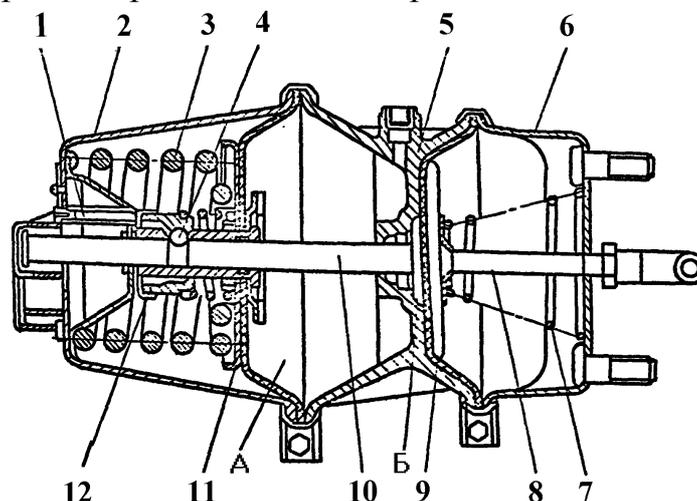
Тормозная камера с пружинным энергоаккумулятором: 1 – направляющая; 2 – цилиндр энергоаккумулятора; 3 – силовая пружина; 4 – шарик; 5 – фланец; 6 – корпус тормозной камеры; 7 – возвратная пружина; 8 – шток; 9 – подпятник; 10 – толкатель; 11 – поршень; 12 – втулка скользящая; А, Б – полости
